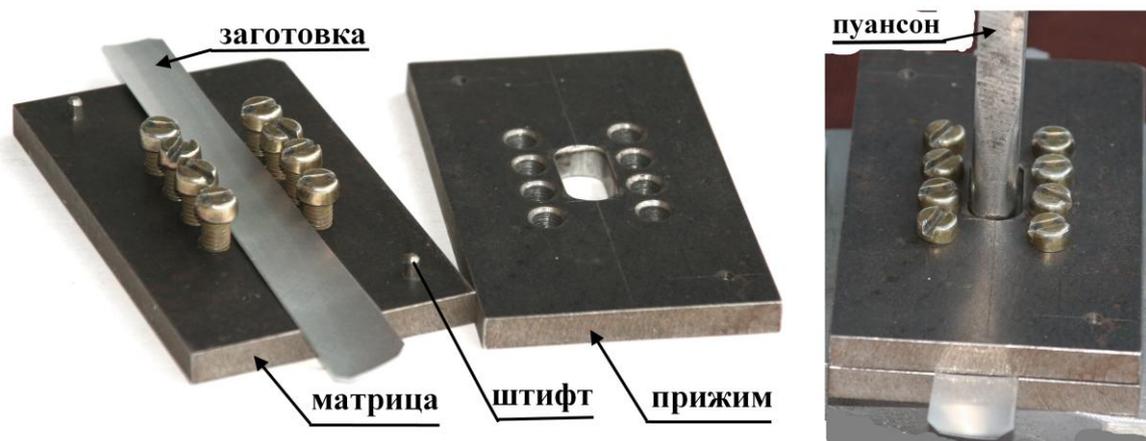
Штамп для изготовления детали типа «лодочка».
